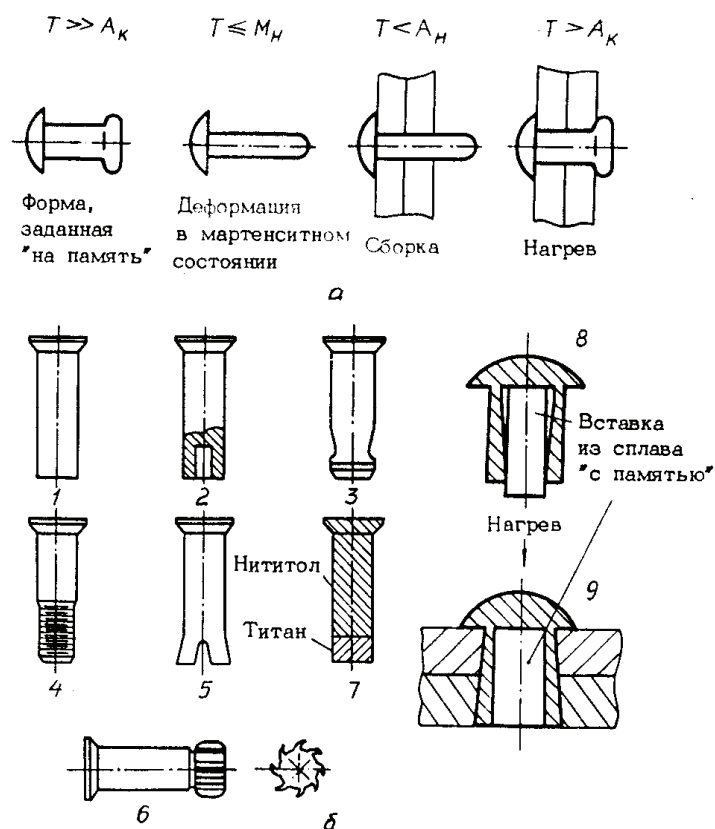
Схема получения заклёпочного соединения с использованием сплава с памятью (а) и различные конструкции заклёпок (б): 1 - стандартная (NAS 1199); 2 - с полой высадной головкой; 3 - "Хайшир" (NAS 1106); 4 - "Хай-лок" (HL 499); 5 и 6 - с конической и ребристой высадными головками; 7 - составная, с использованием сплава на основе никелида титана; 8 и 9 - комбинированная, с внутренней вставкой из сплава с памятью
